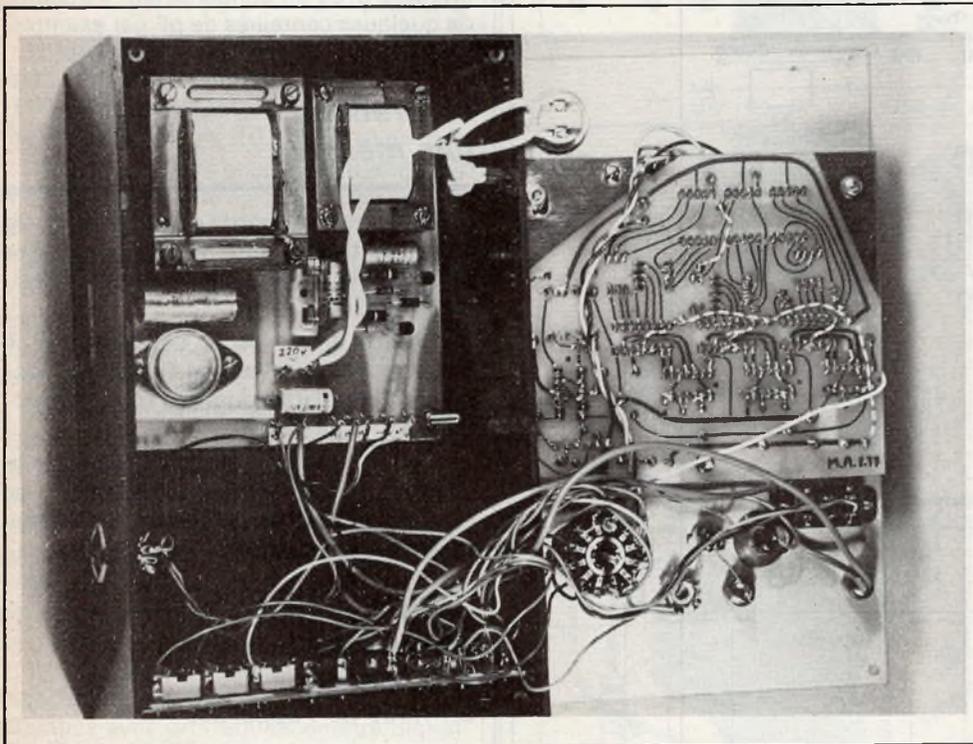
Le boîtier ouvert montre la disposition de chaque élément.
